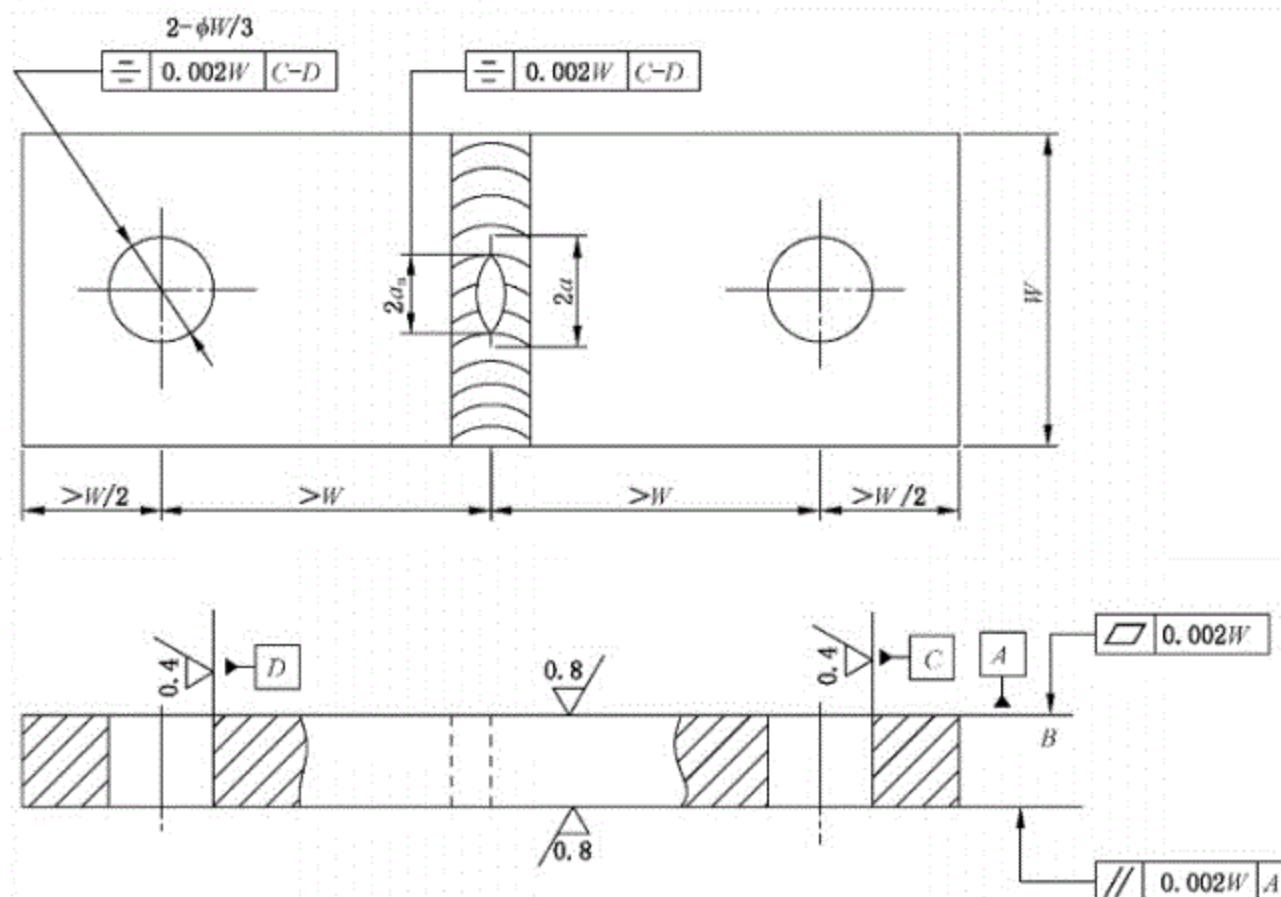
焊接接头疲劳裂纹扩展速率试样(CCT 样)
